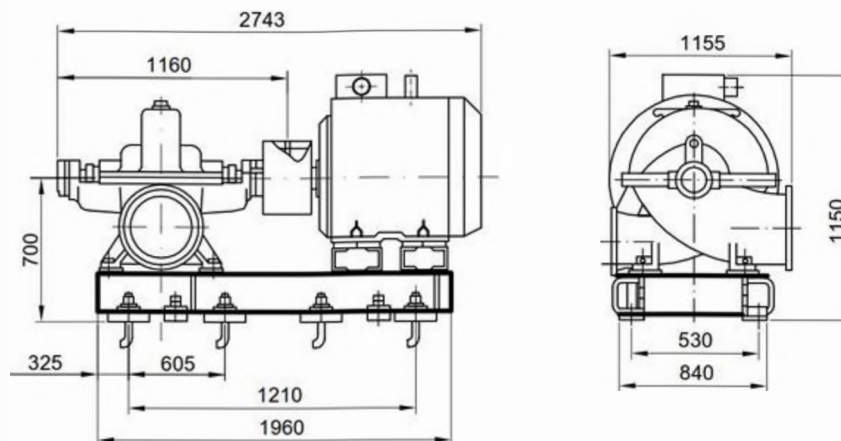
Габаритные и привязочные размеры насоса Д800-57
